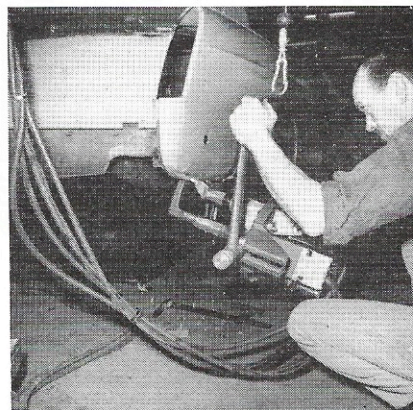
Soudage de l'aile avec le passage de roue. Pince ARO.
